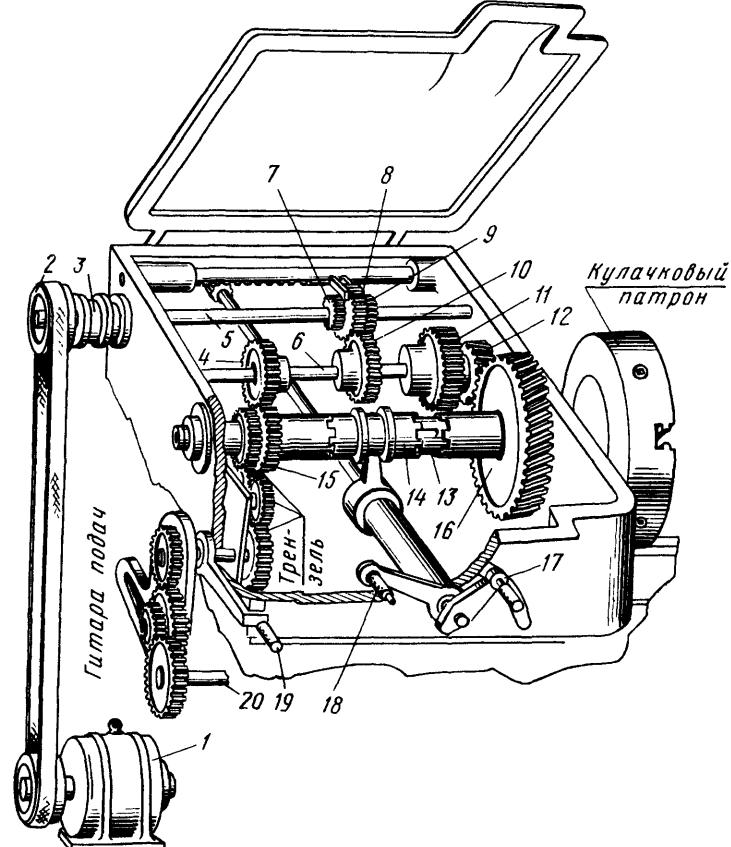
Устройство шестискоростной коробки скоростей токарного станка
